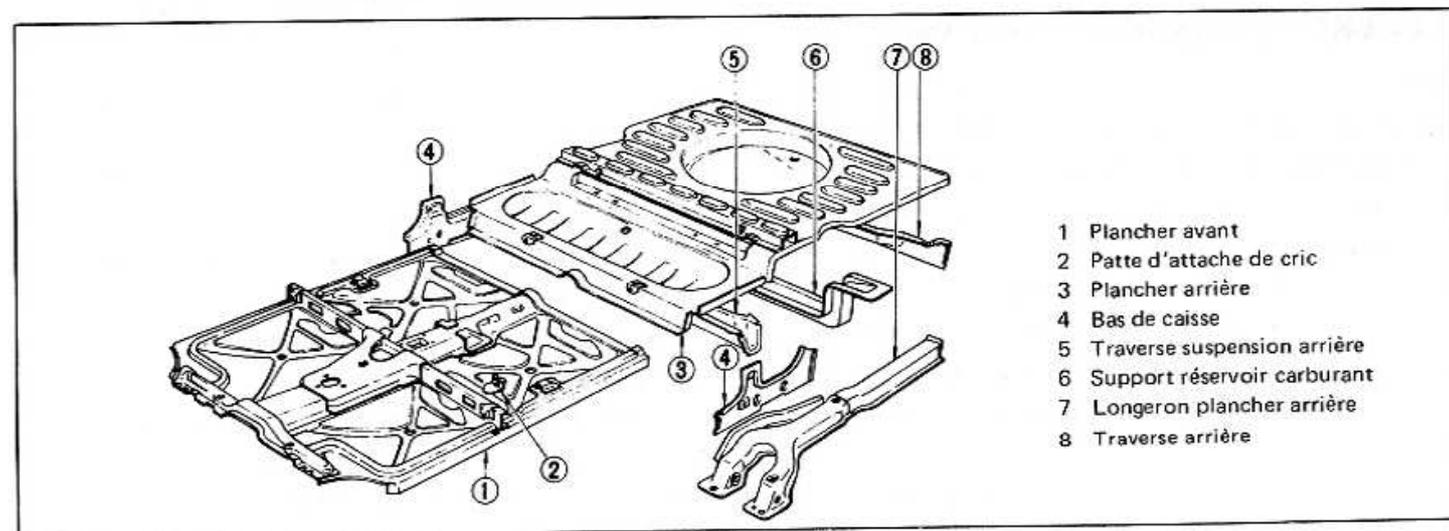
Construction du plancher de carrosserie (Coupé)
